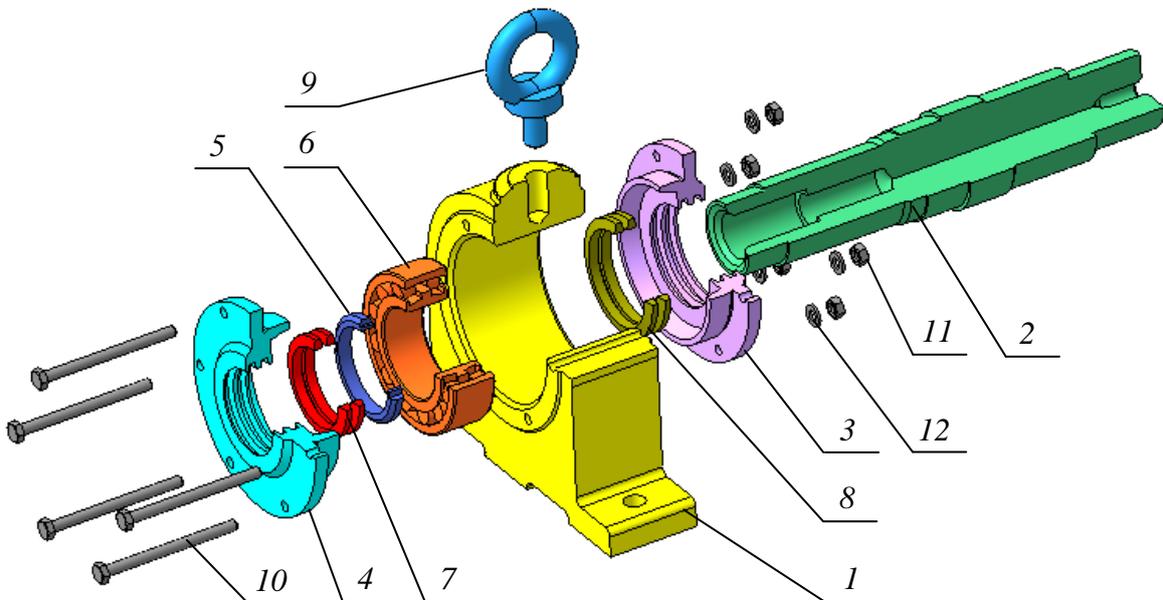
Трехмерная модель сборочного узла «Узел подшипниковый» в разнесенном виде: 1 – корпус; 2 – вал; 3 – крышка правая; 4 – крышка левая; 5 – втулка упорная; 6 – роликовый двухрядный подшипник (внутреннее кольцо, внешнее кольцо и ролик); 7 – кольцо сальниковое левое (2 шт.); 8 – кольцо сальниковое правое (2 шт.); 9 – рым-болт М12 ГОСТ 4751–73; 10 – болт М6 ×80 ГОСТ 7805–70 (6 шт.); 11 – гайка М6 ГОСТ 5915–70 (6 шт.); 12 – шайба 6 ГОСТ 11371–78 (6 шт.)
